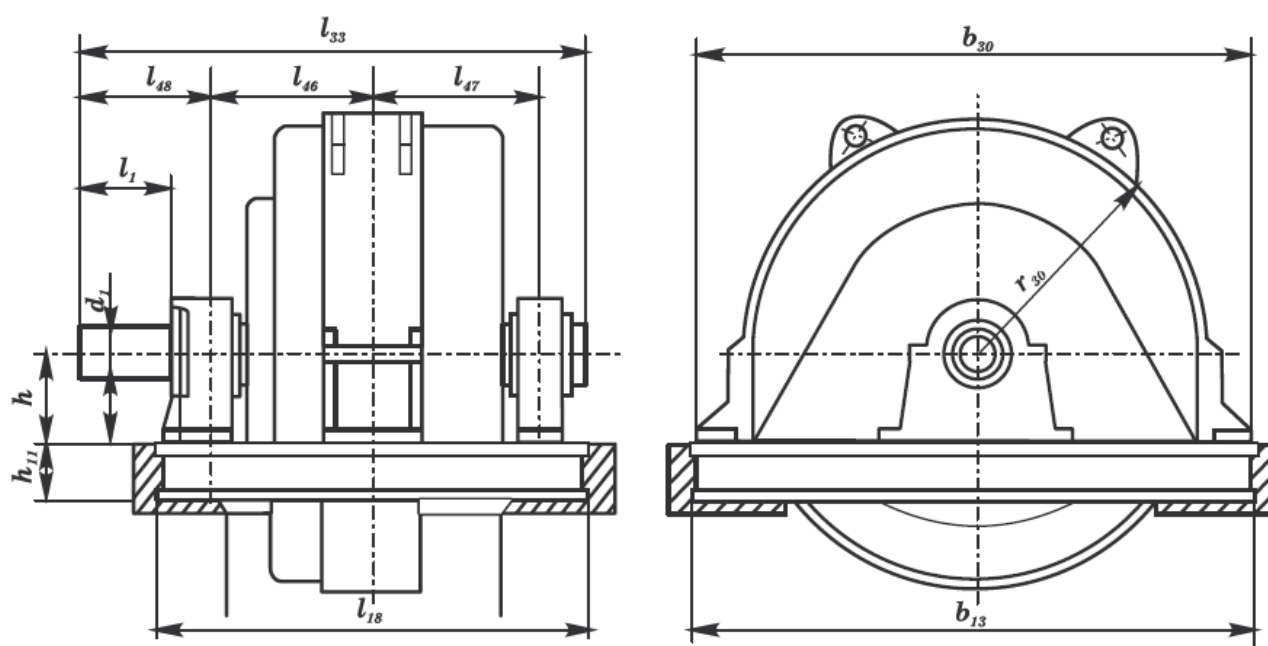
Габаритные, установочные и присоединительные размеры неререверсивных двигателей постоянного тока ряда П2 20, 21 и 24 габаритов
